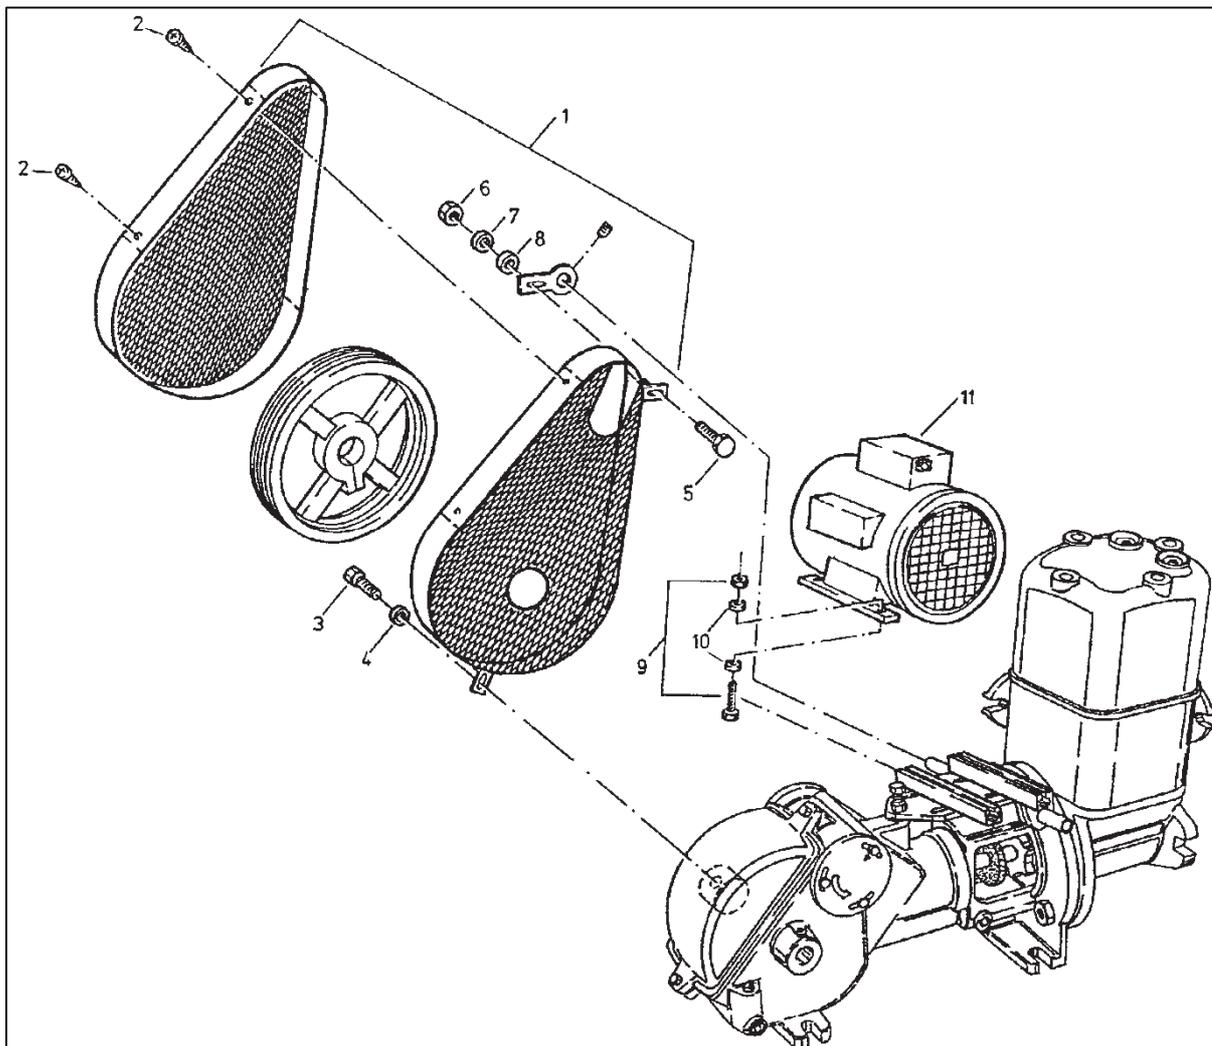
Explosionszeichnung Motoraufbau LG 500-750
